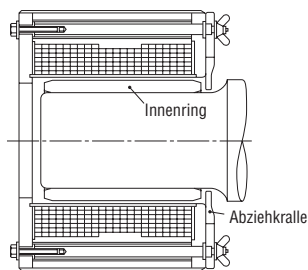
Demontage des Innenrings mit Abziehwerkzeug (2)
